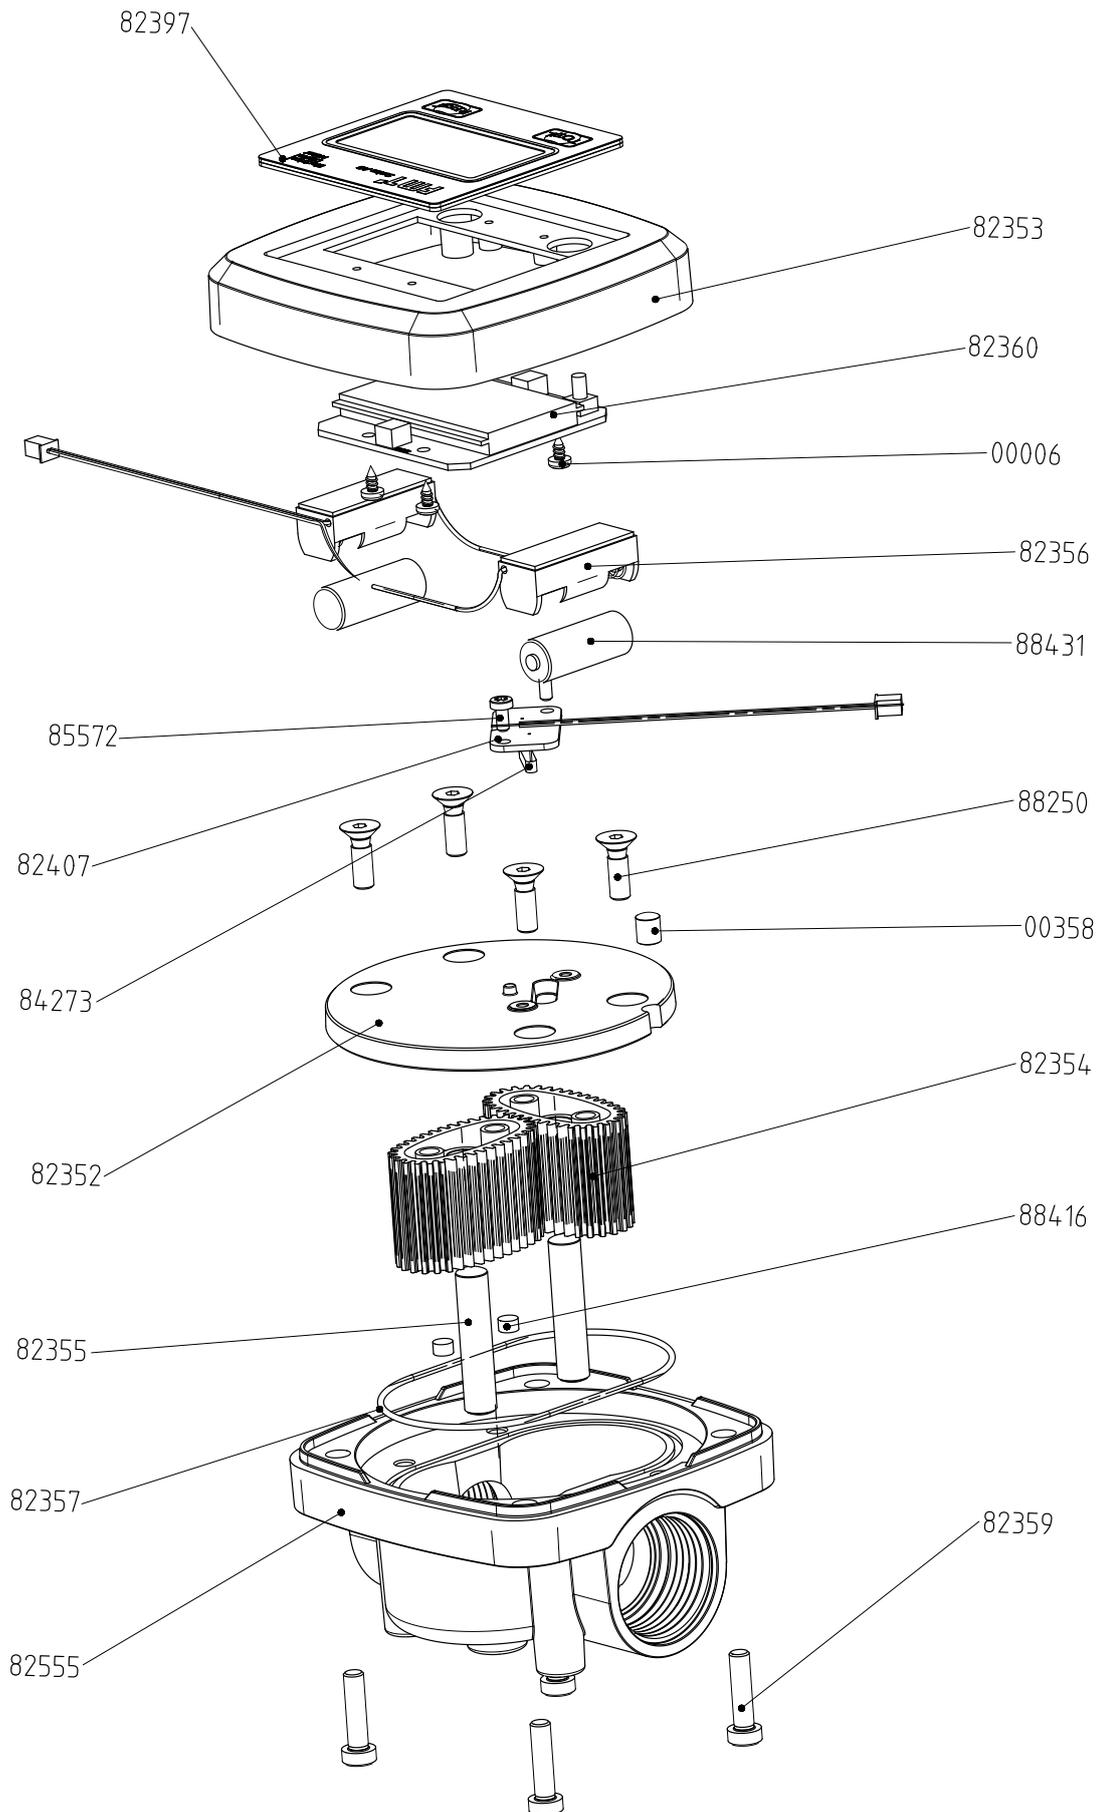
Representación del despiece del contador de engranaje oval
